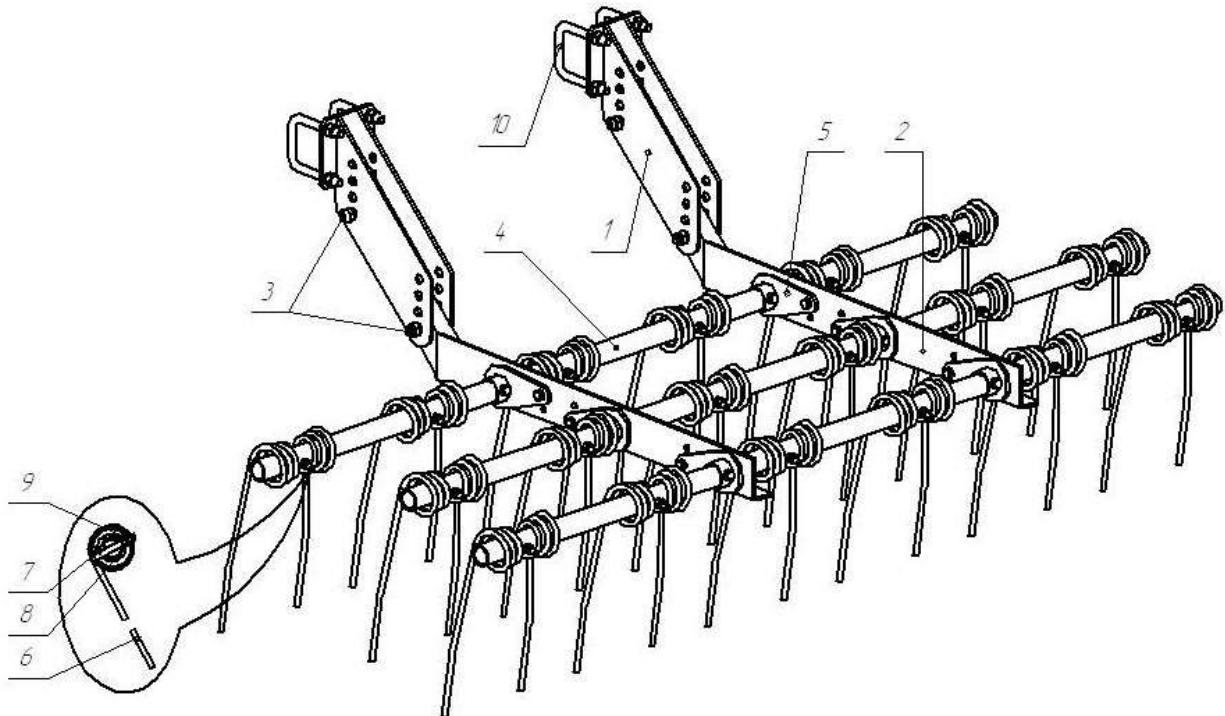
Бороновальный модуль КПП-150.00.000
